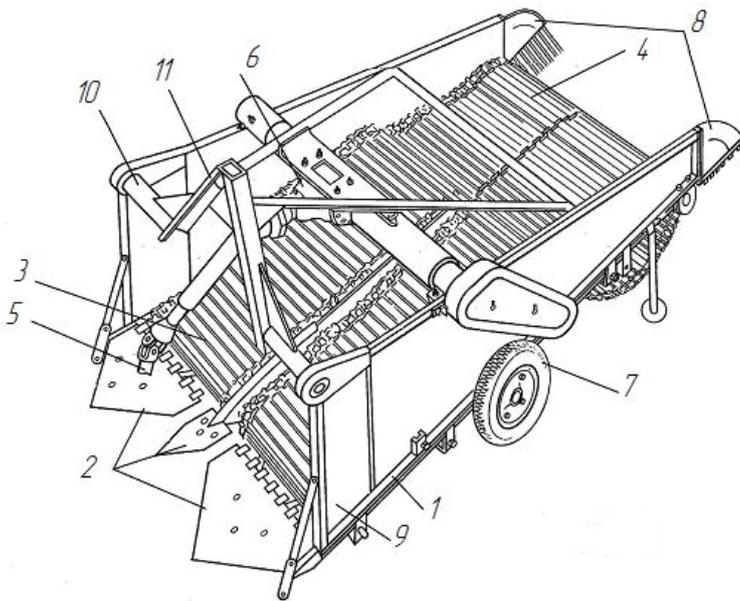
Картофелекопатель КТН-2В [1]: 1 – рама, 2 – три лемеха, 3 – основной элеватор, 4 – каскадный элеватор, 5 – карданная передача, 6 – редуктор, 7 – опорные колеса, 8 – отражатели, 9 – боковины рамы, 10 – поперечный брус, 11 – прицепное устройство А-образной формы
